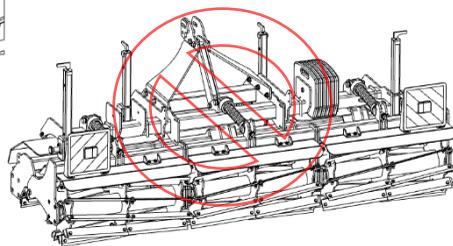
Beispiel für die falsche Anbringung von Gewichten.
